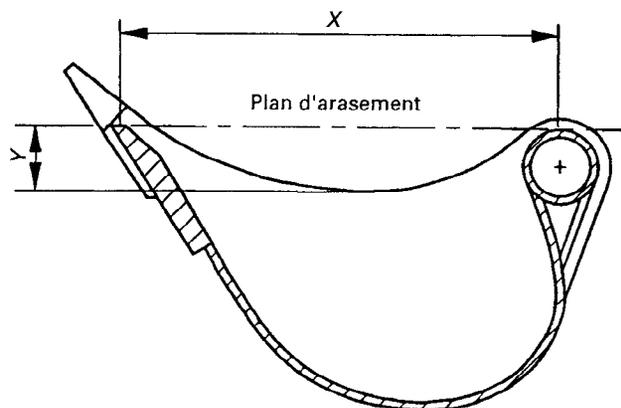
Détermination de la position du godet par rapport au plan horizontal
